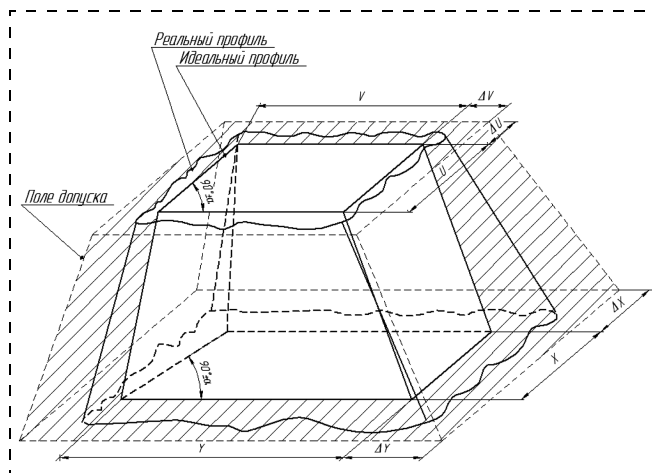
Погрешность геометрической формы обрабатываемой детали
